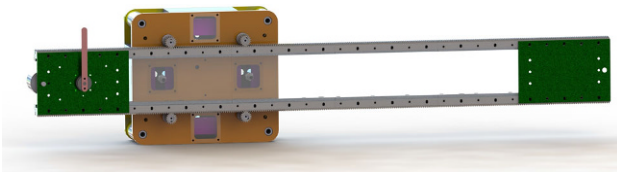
3D CAD-Modell des Linear-Planetenmotors
